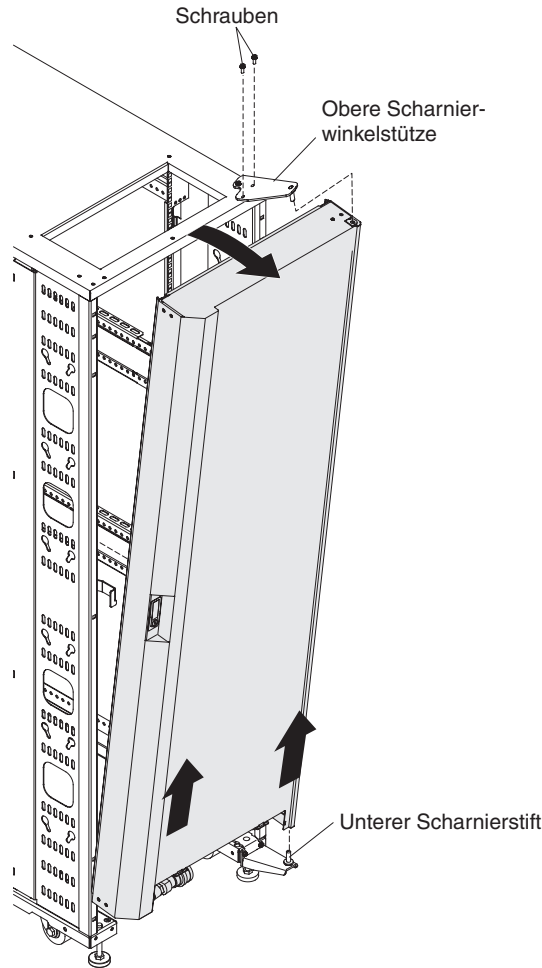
Wärmetauscher aus dem Gehäuserahmen entfernen
